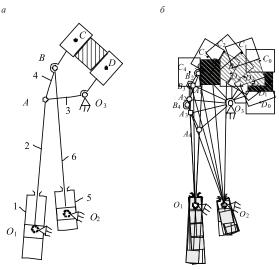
Схема роликового кантователя прокатного стана (а) и построение положений механизма для режима кантовки заготовки (б)
